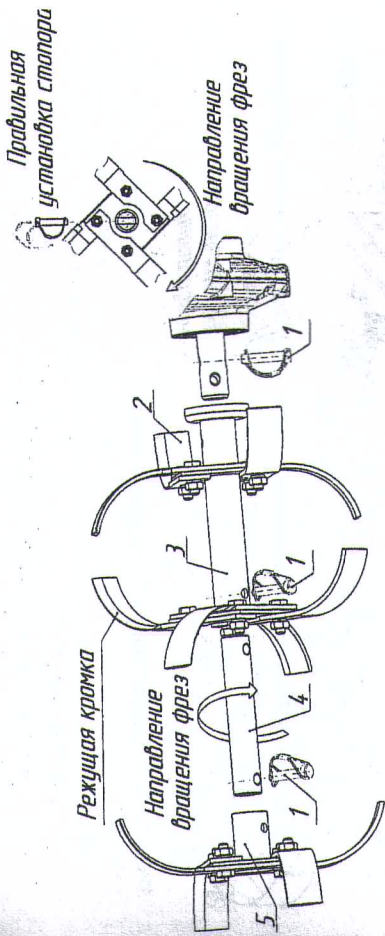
Установка 6-ти фрез-культиваторов. 1 – стопор; 2 – фреза; 3 – культиватор двойной; 4 – переходник; 5 – культиватор одиночный (направление вращения фрез см. на рис. 14)
